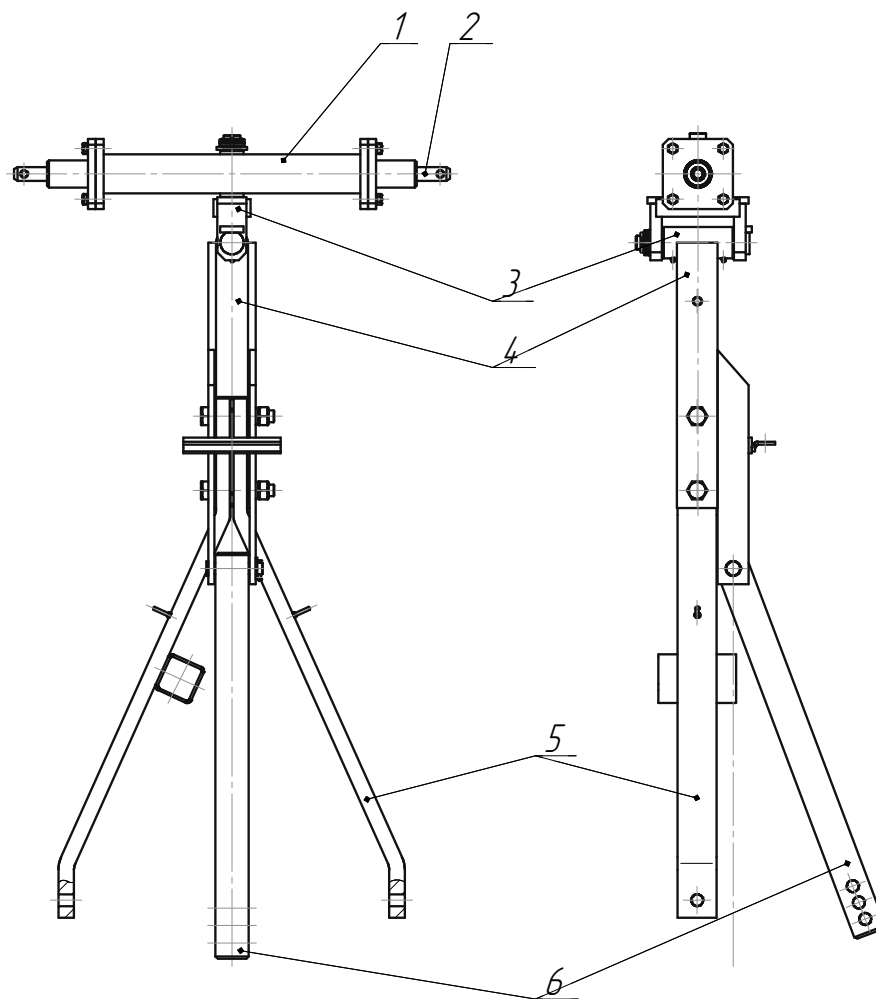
Причіпний пристрій культиватора КП-8,5
